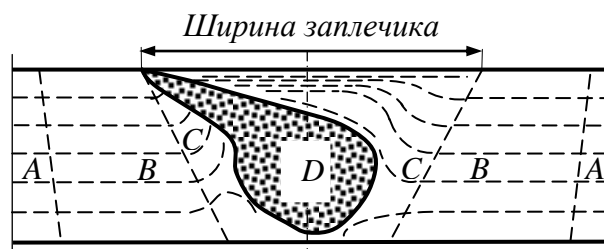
Схема будови зварного з'єднання при зварюванні тертям перемішуванням
